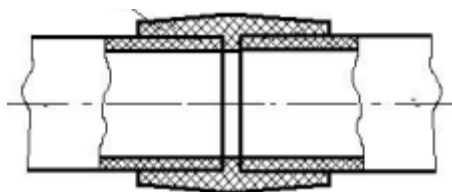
Сварка труб с соединительной муфтой
